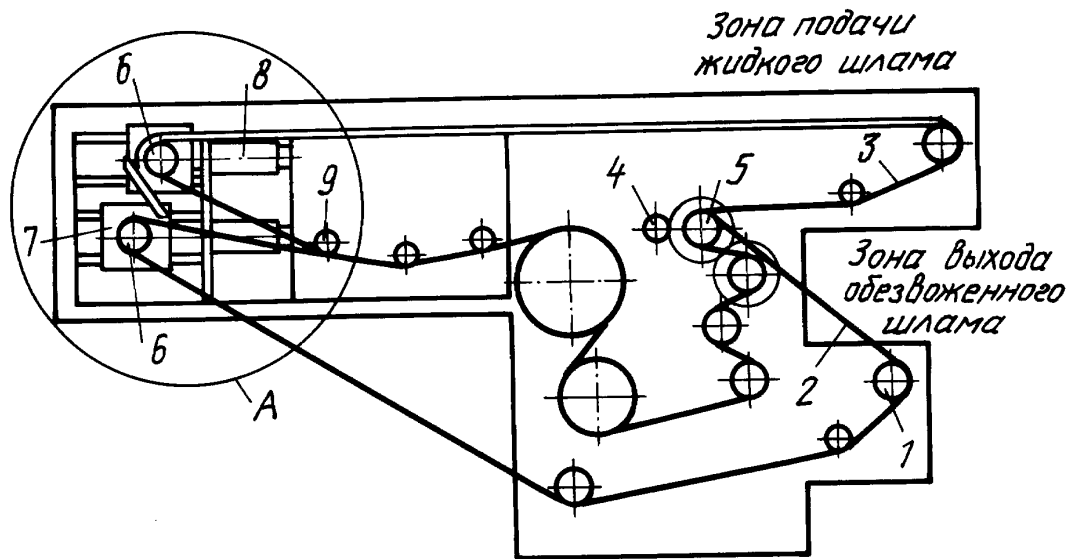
Кинематическая схема ленточного пресс-фильтра с обозначением зоны размещения подвижных опор с валами натяжения ленточных сит
